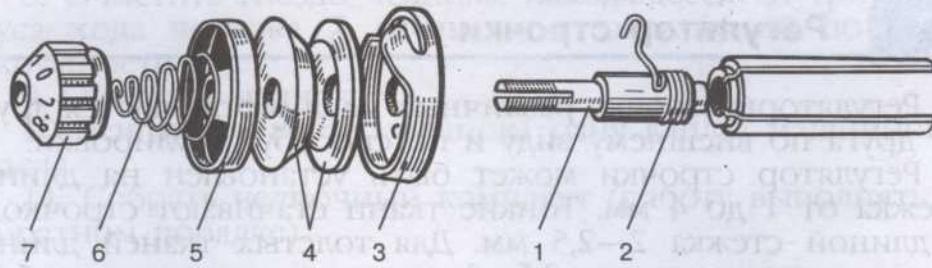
Регулятор натяжения верхней нитки бытовой швейной машины класса 2М-ПМЗ:
